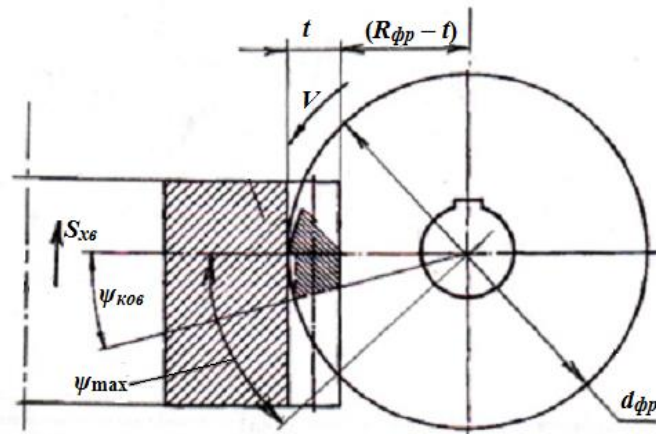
Схема розрахунку параметрів обробки при зубофрезеруванні відновлених зубчастих коліс
